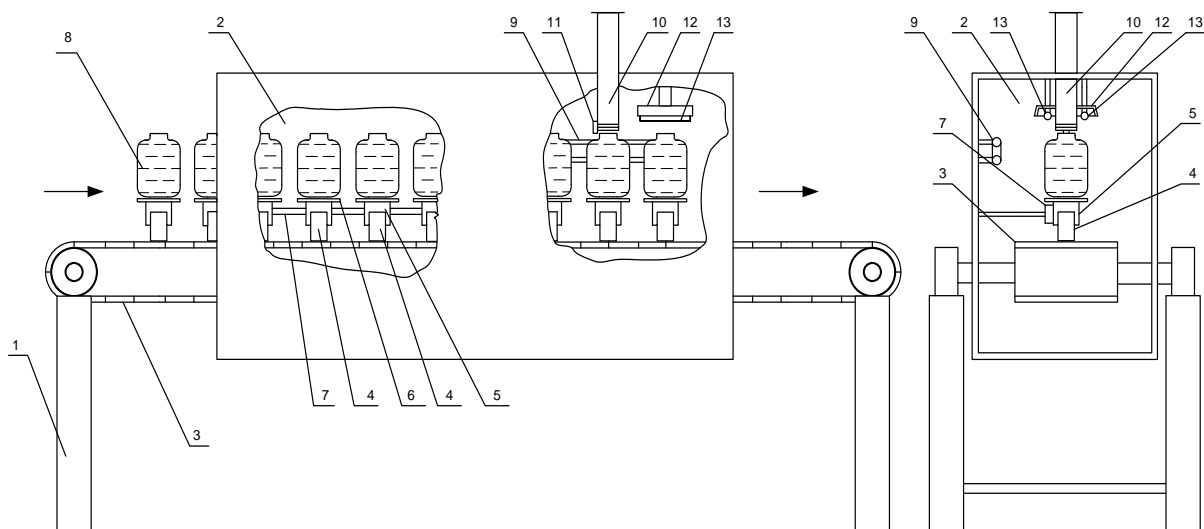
Аппарат для СВЧ-нагрева консервируемых продуктов: 1 – станина; 2 – камера СВЧ-обработки; 3 – транспортирующий орган; 4 – втулки упорных пластин; 5 – упорные пластинки; 6 – приемный столик банок; 7 – направляющая для банок; 8 – банки; 9 – нагреватель электрический; 10 – магазин крышек; 11 – механизм подачи крышек; 12 – отражатель; 13 – инфракрасные лампы
